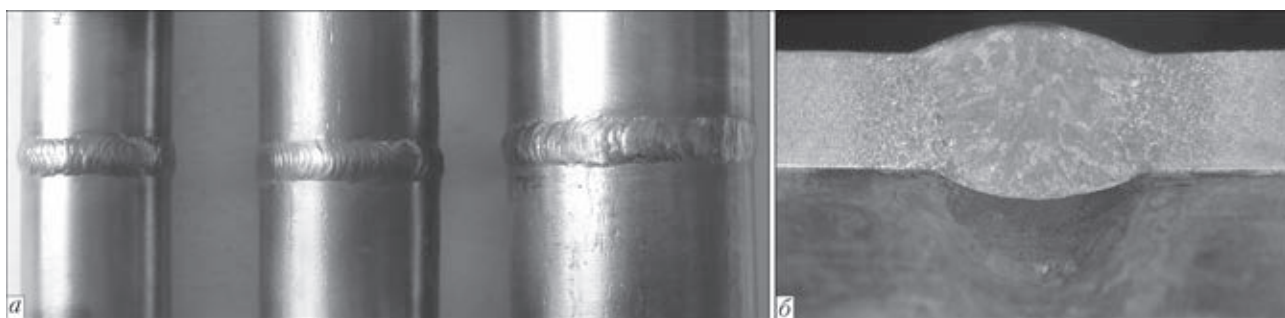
Стыковые соединения труб поверхности нагрева: а — внешний вид соединений; б — поперечное сечение соединения
